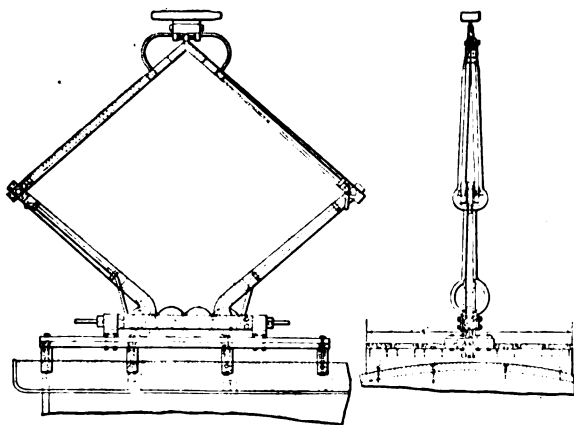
et 8. — Vue latérale et vue en bout du trôlet.
